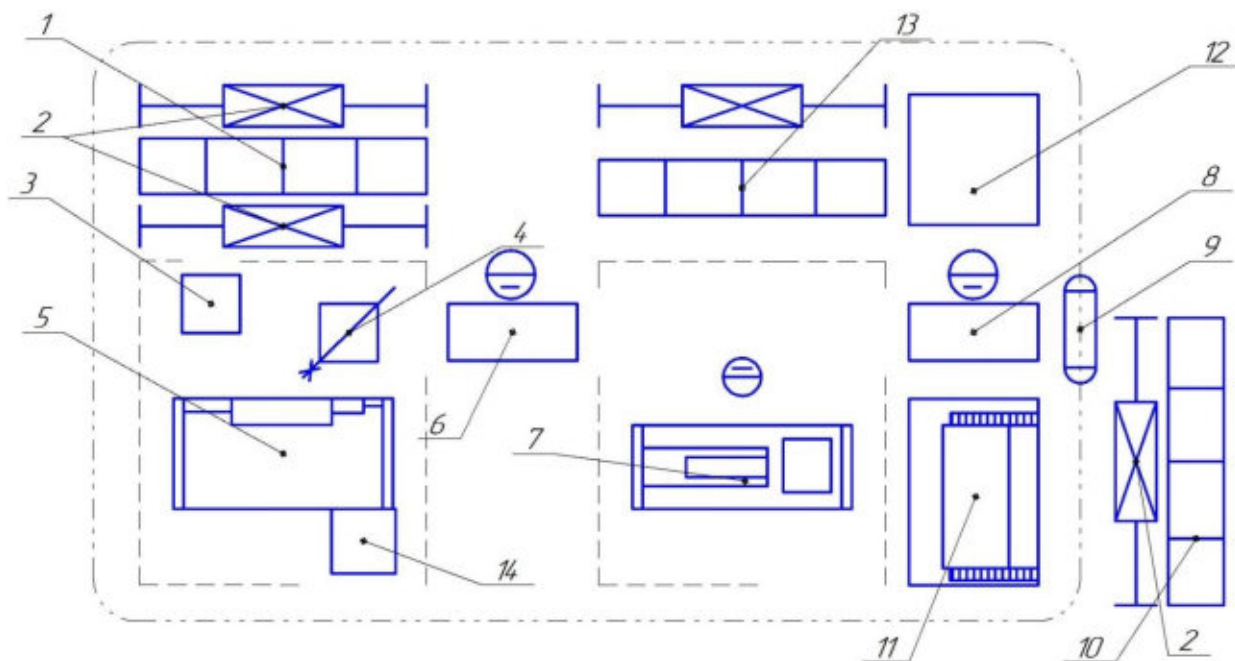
Первый вариант расположения оборудования (1-склад заготовок; 2-робот-штабелер; 3-приемно-раздаточный стол; 4-промышленный робот; 5-первый обрабатывающий центр с ЧПУ; 6-первый стол промежуточного контроля; 7-второй обрабатывающий центр с ЧПУ; 8-второй стол промежуточного контроля; 9-автокар; 10-промежуточный склад хранения; 11-моечная установка; 12-пункт окончательного контроля; 13-склад готовой продукции; 14-бак для стружки)
